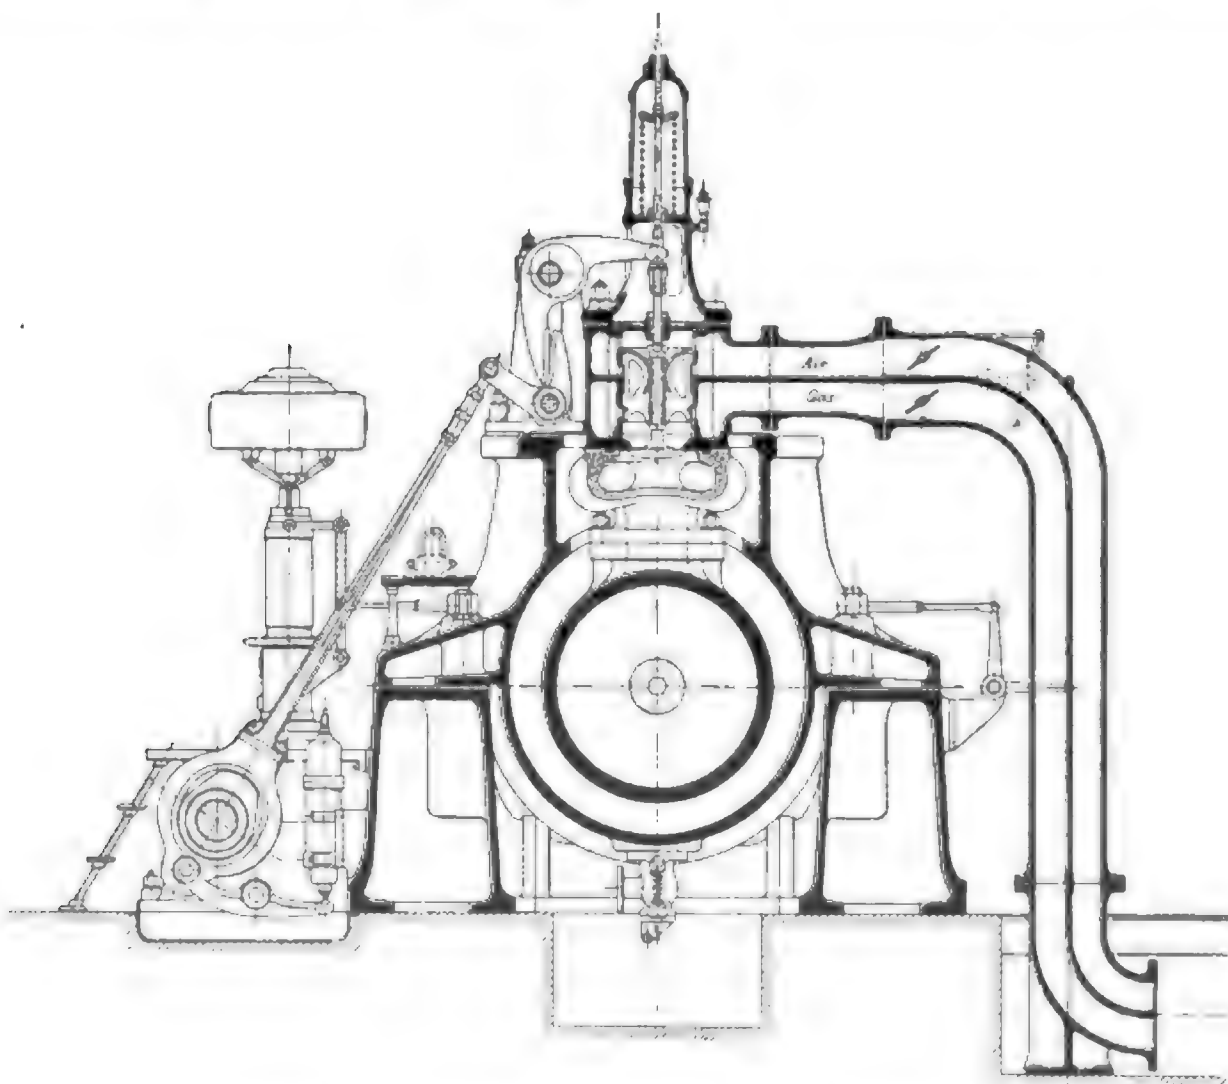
Steuerung zum Gasmotor von Fried. Krupp, Akt.-Ges.
